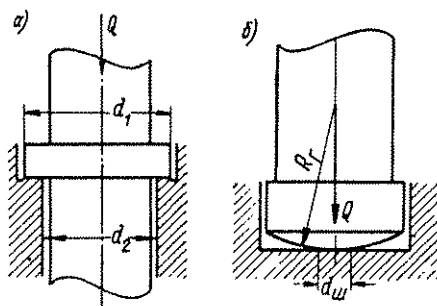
Схема работы пята: а — кольцевой; б — шаровой
